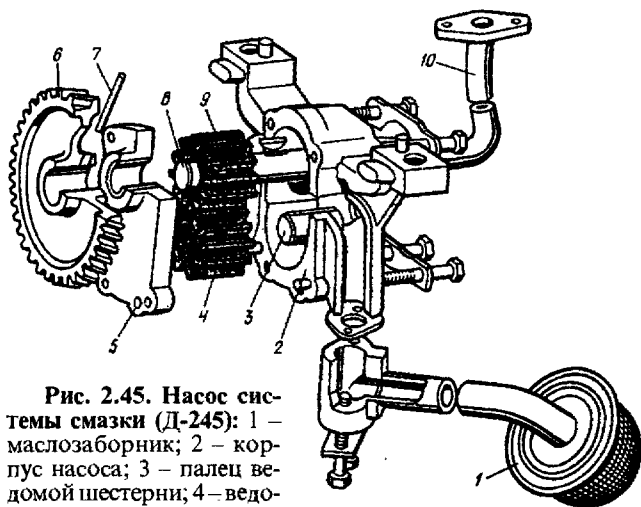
Насос системы смазки (Д-245): 1 – маслозаборник; 2 – корпус насоса; 3 – палец ведомой шестерни; 4 – ведомая шестерня; 5 – крышка корпуса; 6 – шестерня привода насоса; 7 – штифт; 8 – вал насоса; 9 – ведущая шестерня; 10 – патрубок
